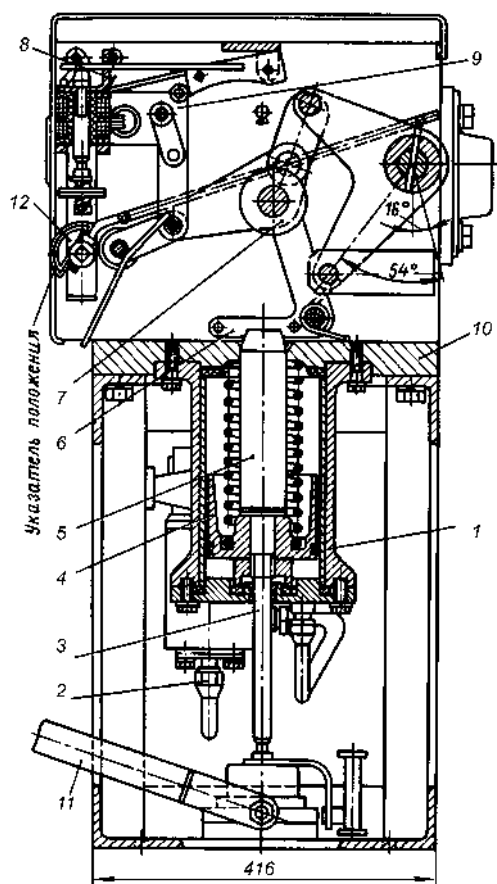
Привод пневматический ПВ-30: 1 – пневматический цилиндр; 2 – фланец воздухопровода; 3 – шток демпфера; 4 – поршень; 5 – шток; 6 – удерживающая защёлка; 7 – подъёмный ролик; 8 – электромагнит отключения; 9 – система рычагов свободного расцепления; 10 – корпус привода; 11 – домкрат для ручного включения; 12 – указатель положения
